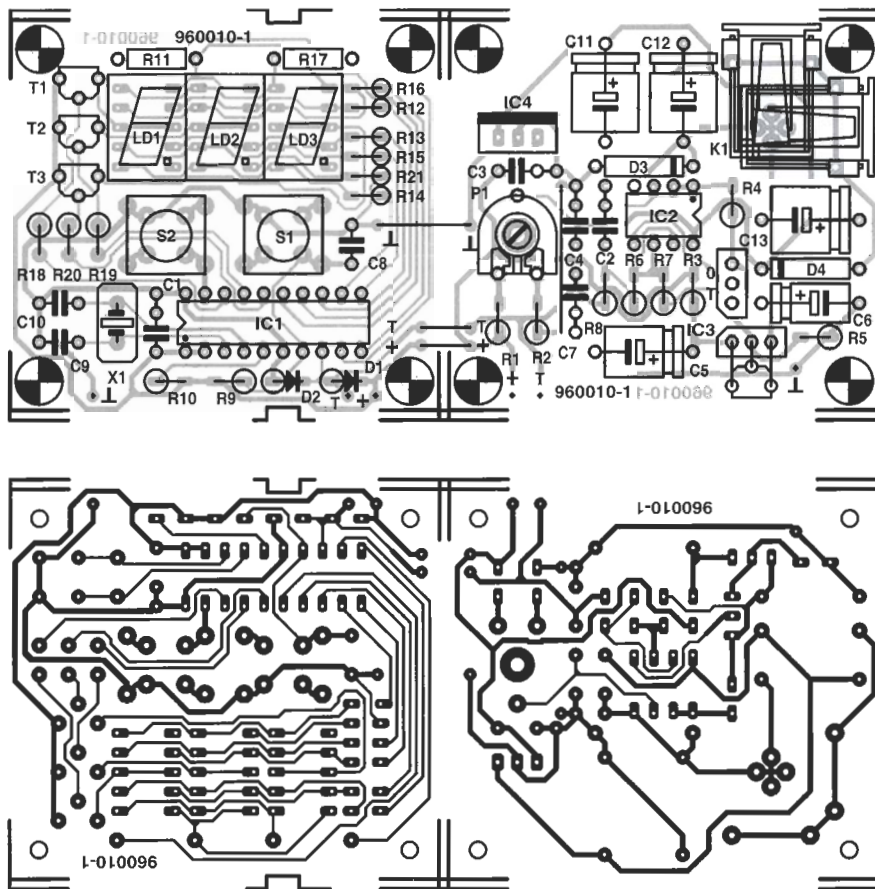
Placa de circuito impreso del montaje. Puede ser montada como una sola placa o partida en dos.
